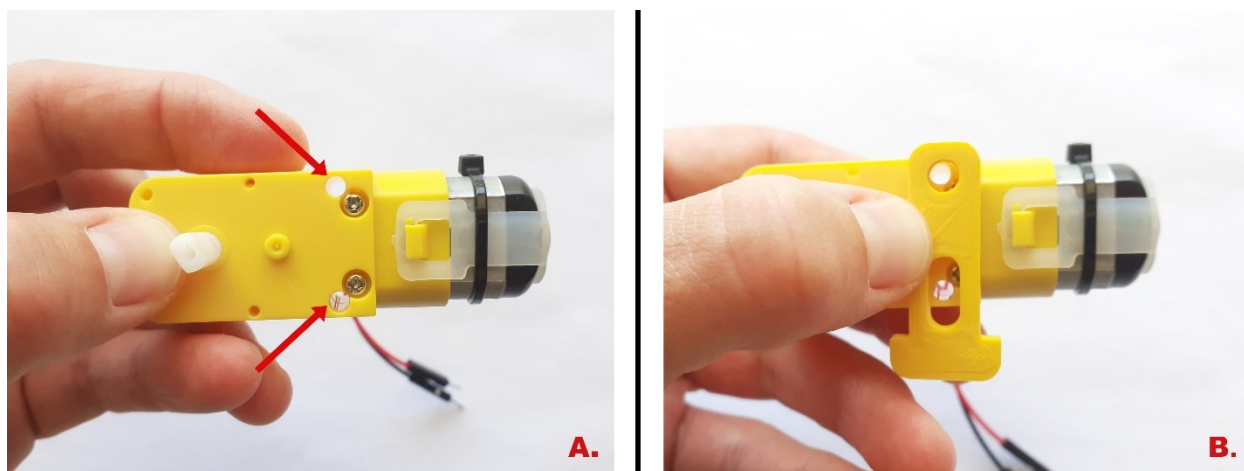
A. Os orifícios de passagem nos motores de engrenagem DC; B. Demonstração da posição dos braços em relação aos motores
